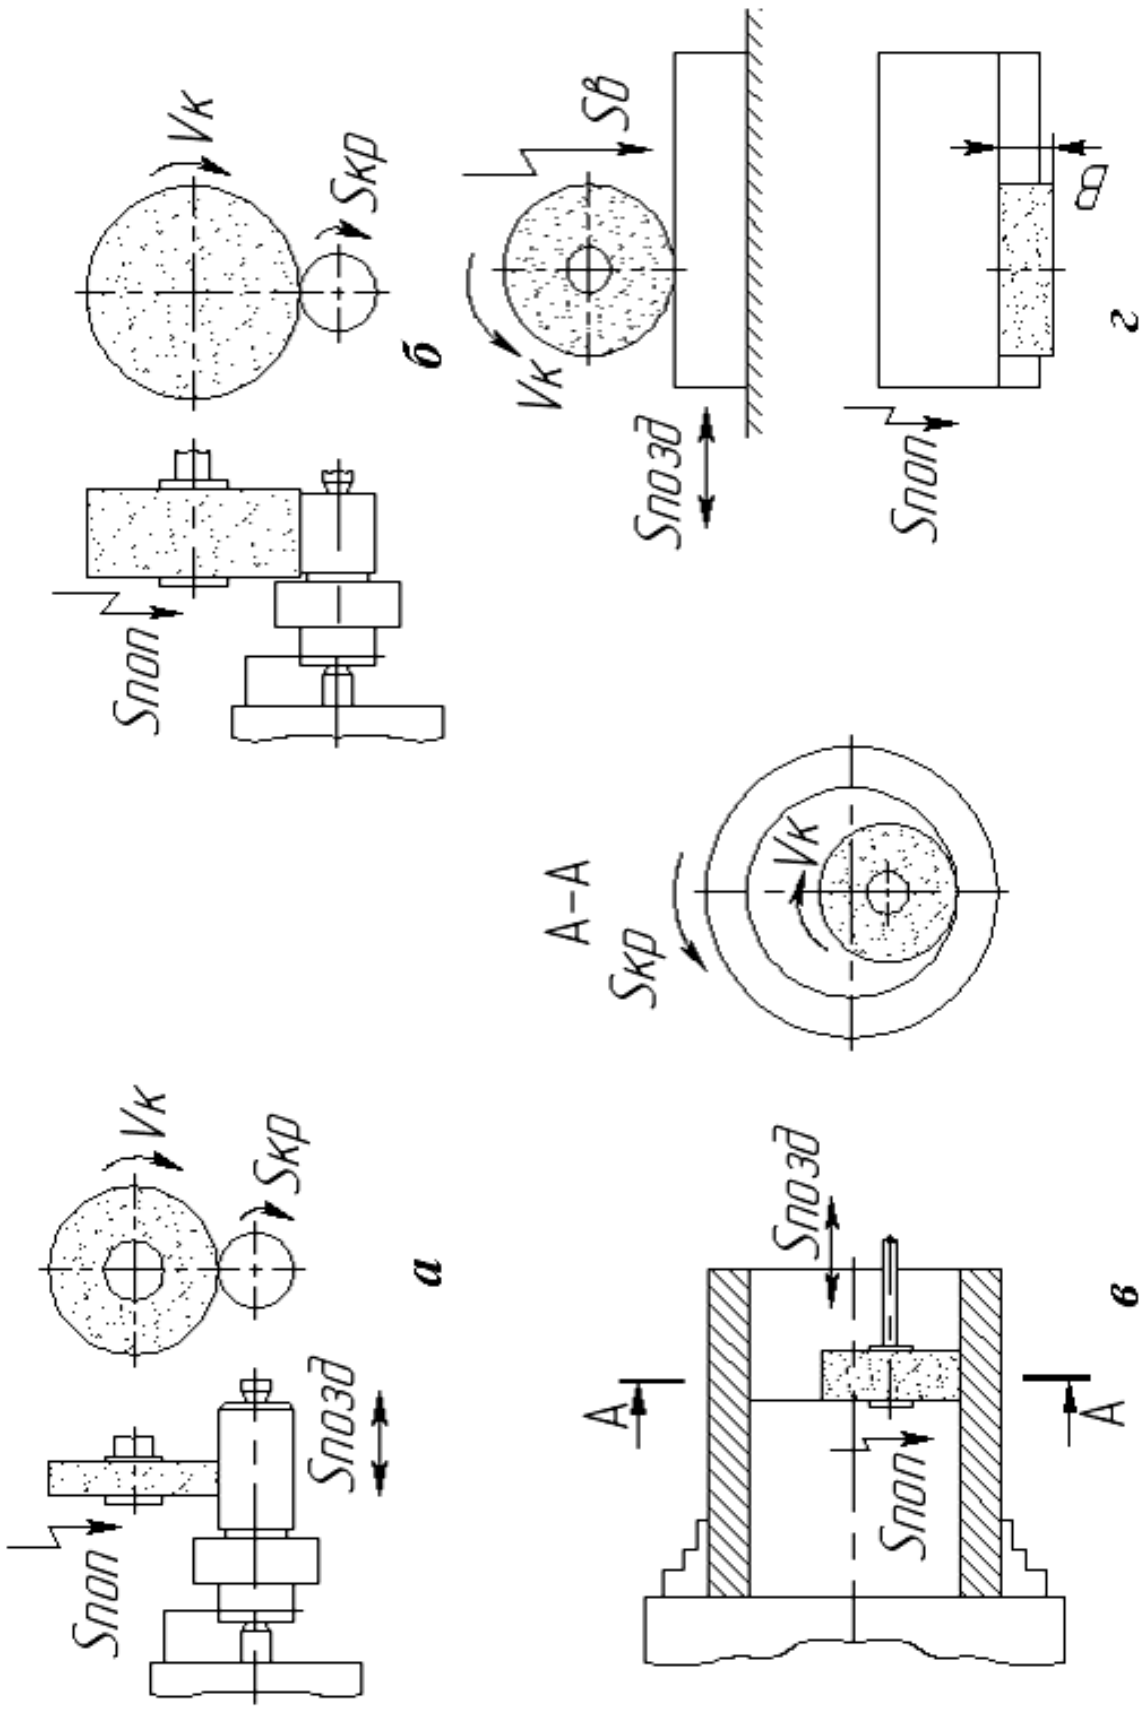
Схеми обробки заготовок на шліфувальних верстатах
